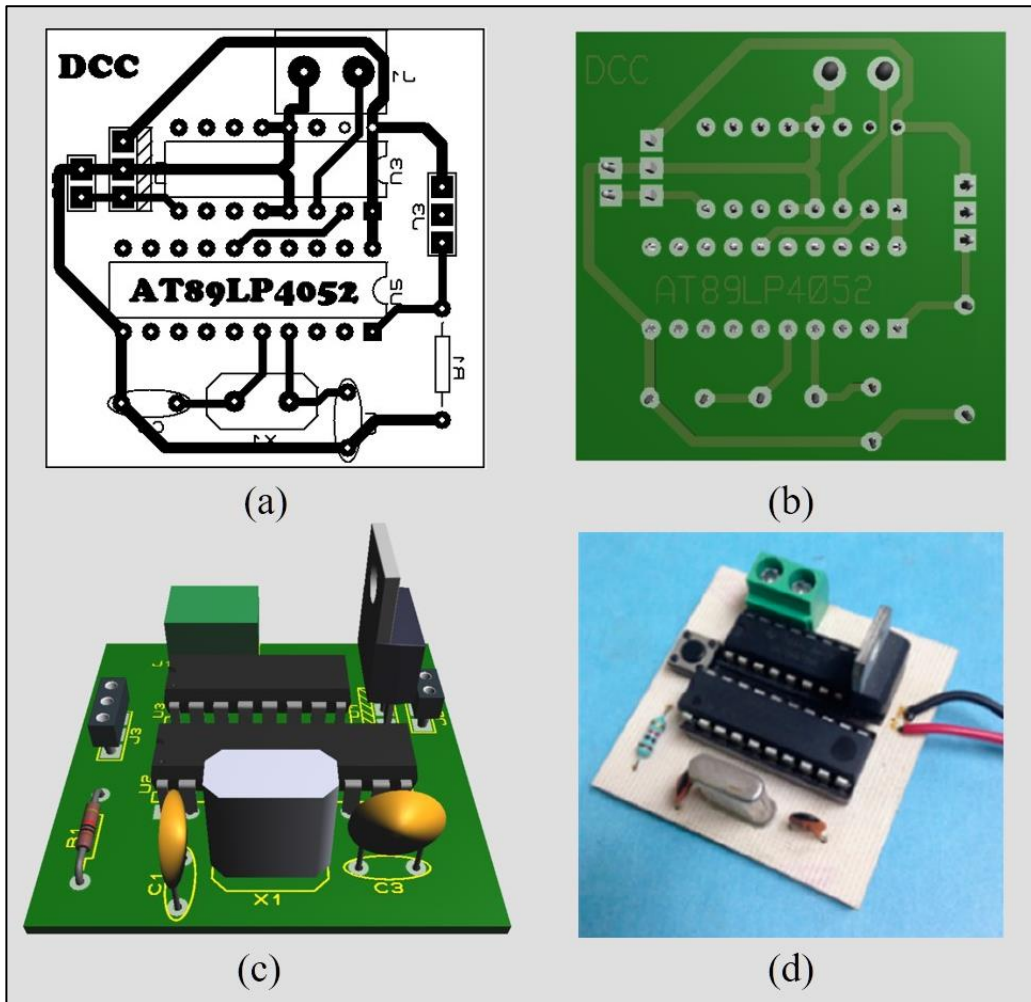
(a) Diseño del PCB. (b) Modelo del diseño del PCB. (c) Vista 3D área del modelo del PCB. (d) Imagen del circuito electrónico.
